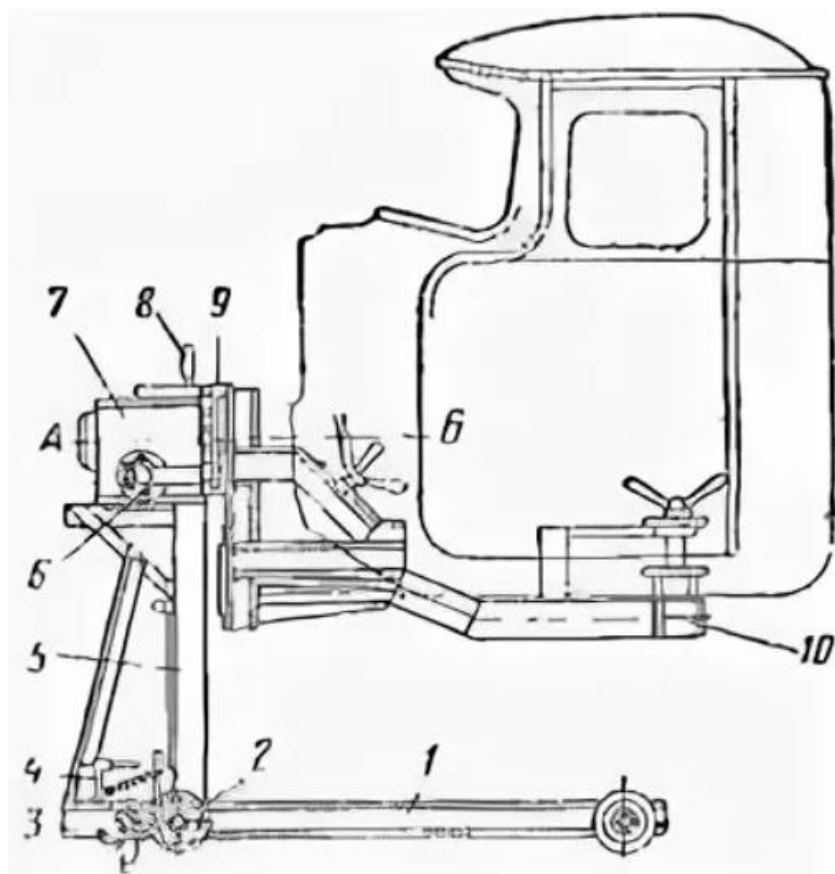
Стенд для ремонта кабин ЗИЛ-130, модель Р-229
